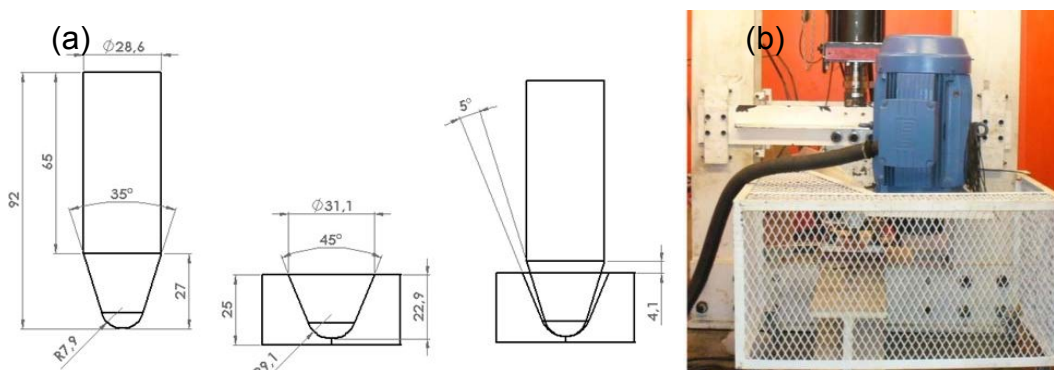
(a) Geometria utilizada para a confecção do pino consumível e da chapa base (medidas em mm); / (b) Equipamento de soldagem MPF 1000.
